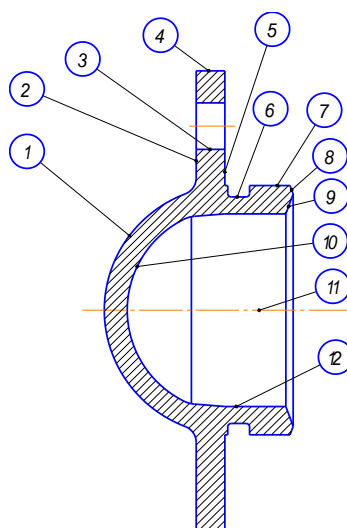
Нумерация поверхностей корпуса специальной кинематической пары
